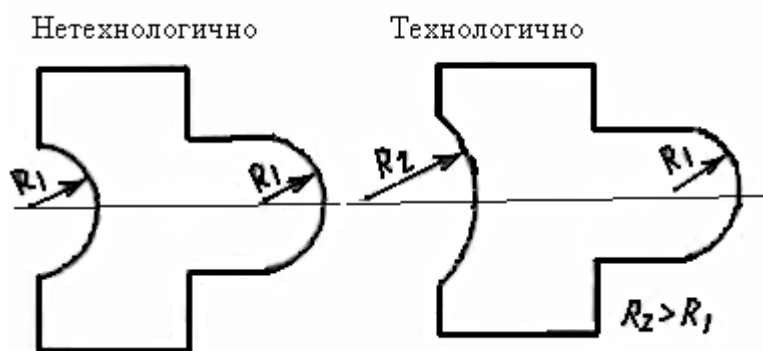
Способ улучшения технологичности конструкции деталей с внутренними и внешними криволинейными поверхностями
